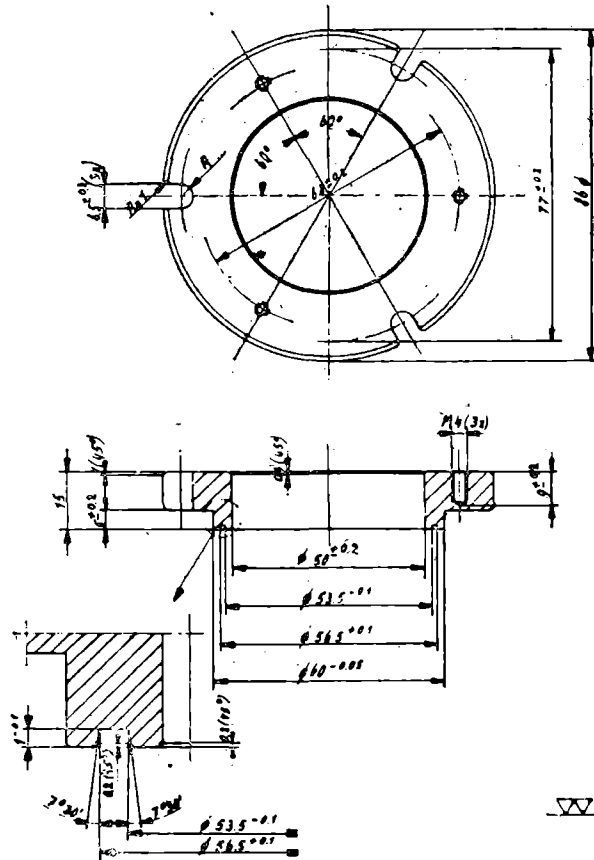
Anillo de presión del recipiente (detalles en sección vertical y en planta). (Dimensiones en mm.)
